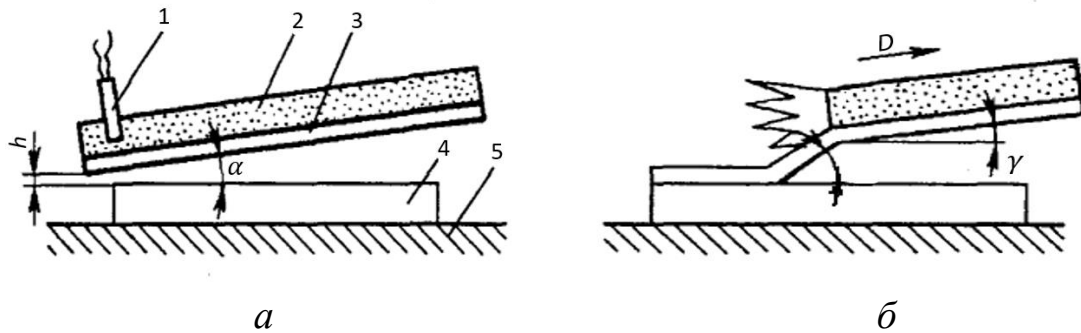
Кутова схема зварювання вибухом до початку (а) і в стадії вибуху (б): 1 – детонатор; 2 – заряд речовини; 3, 4 – зварювані заготовки; 5 – жорстке підставу;  $\gamma$  – кут між пластинами;  $h$  – найменша відстань
